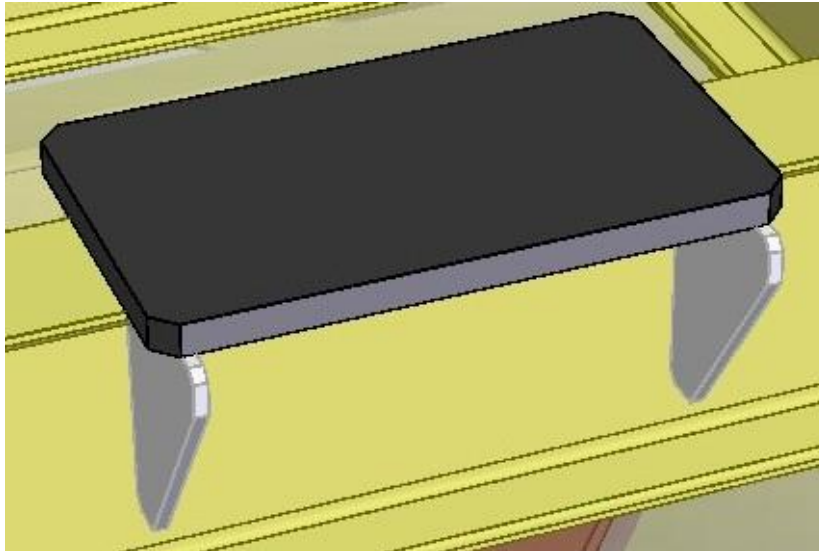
Detalle de cartelas de refuerzo en placas de apoyo
